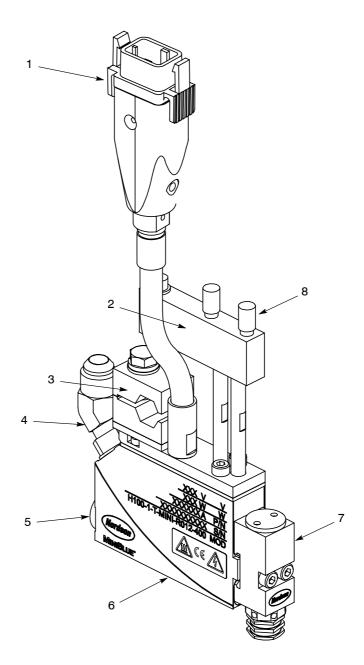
Componenti principali di una pistola MiniBlue sottile a modulo singolo
